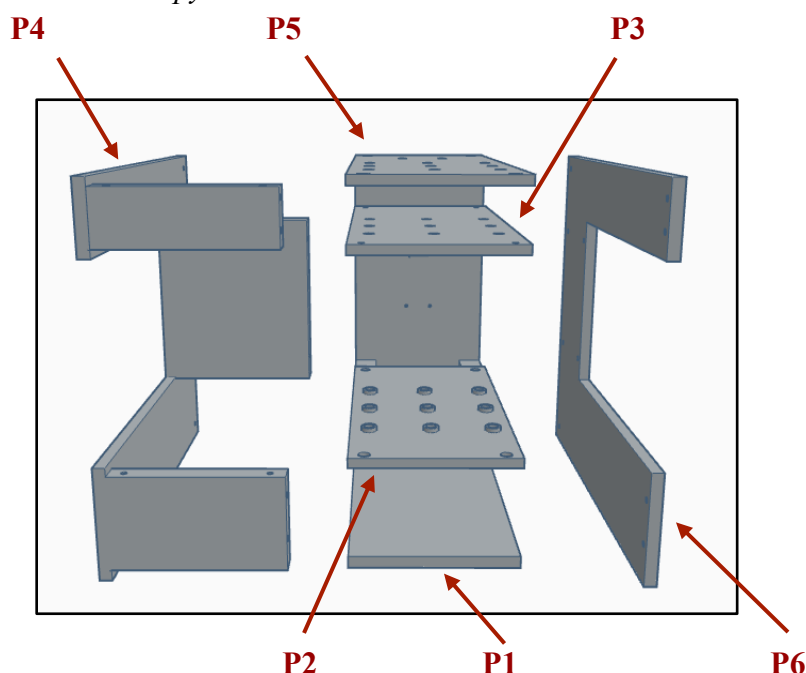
Детали РетнаБокс , напечатанные на 3D-принтере.
